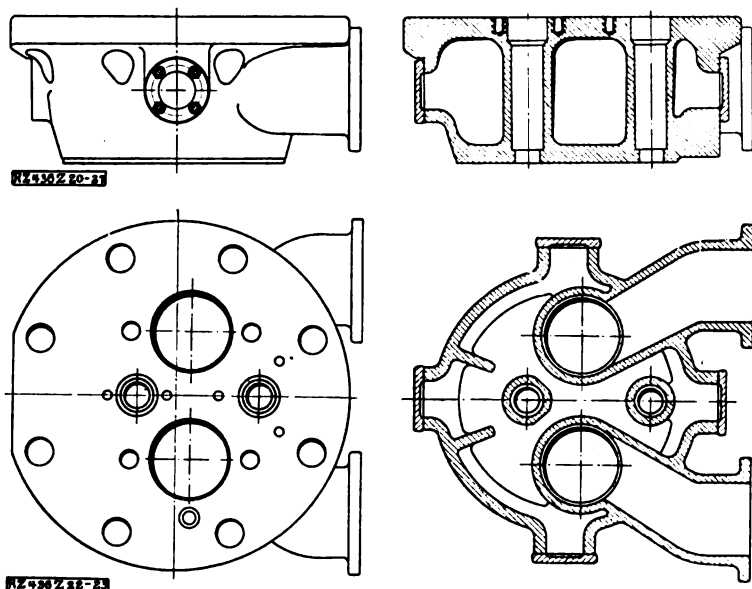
bis 23. Zylinderkopf der Dieselmachine, Abb. 14 bis 16.
